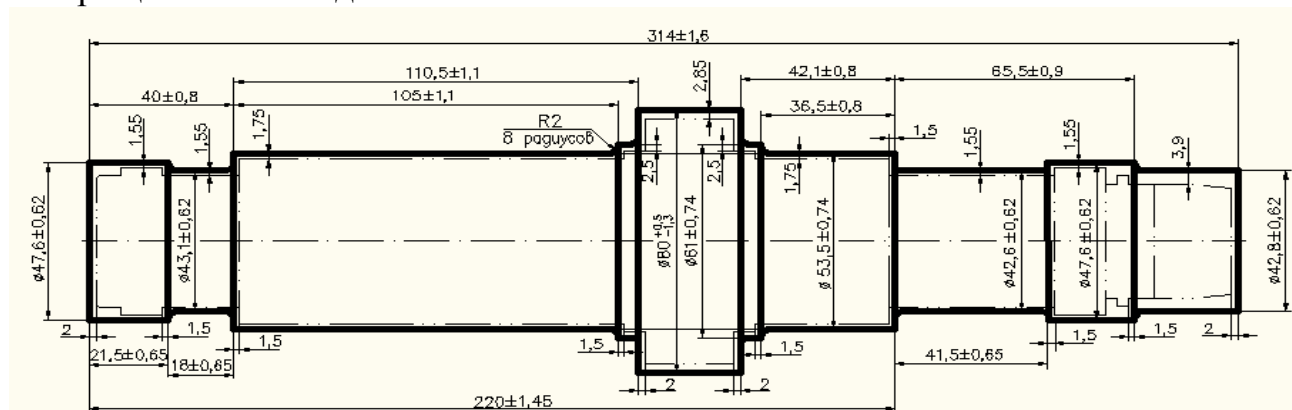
Чертёж поковки получаемый после поперечно-клиновой прокатки
